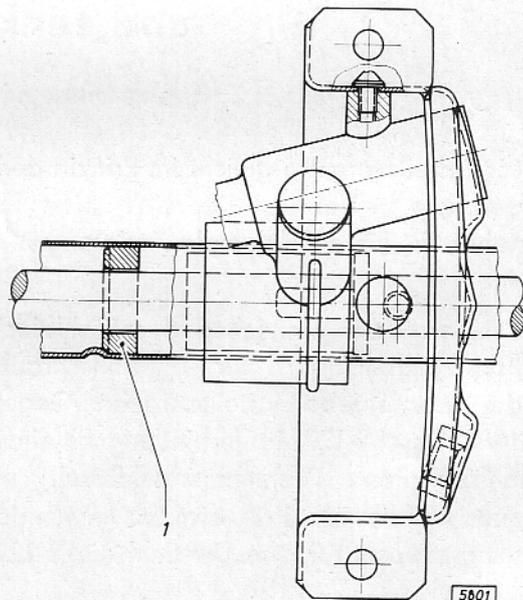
Lage des Lenkspindel-Führungsringes im Lenkstützrohr
